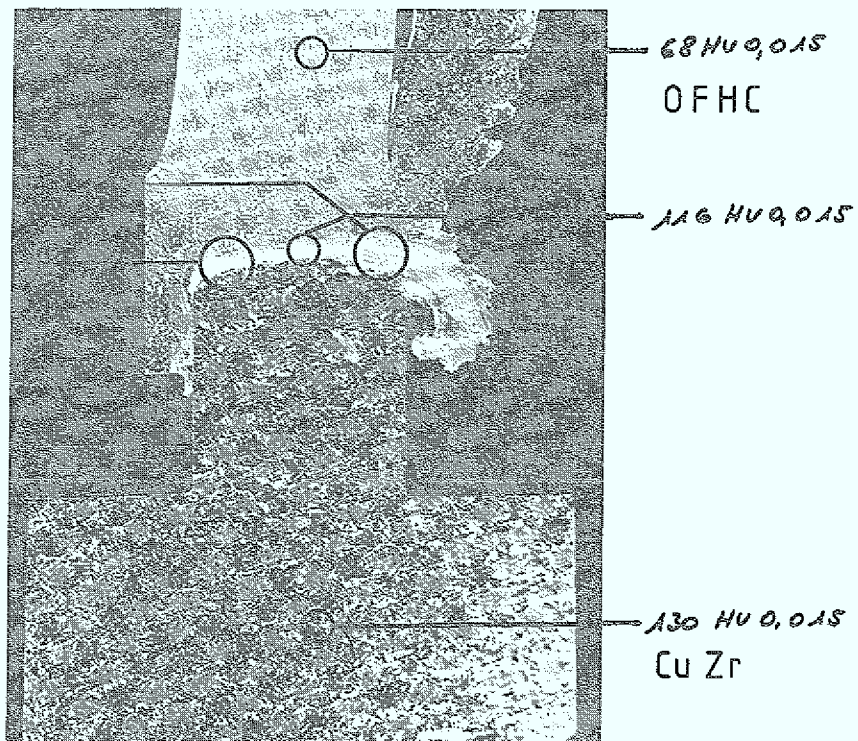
Schliffbilder einer Reibschweißver-
